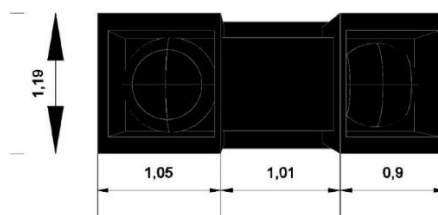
Dimensiones del sensor Sharp visto desde la parte frontal
